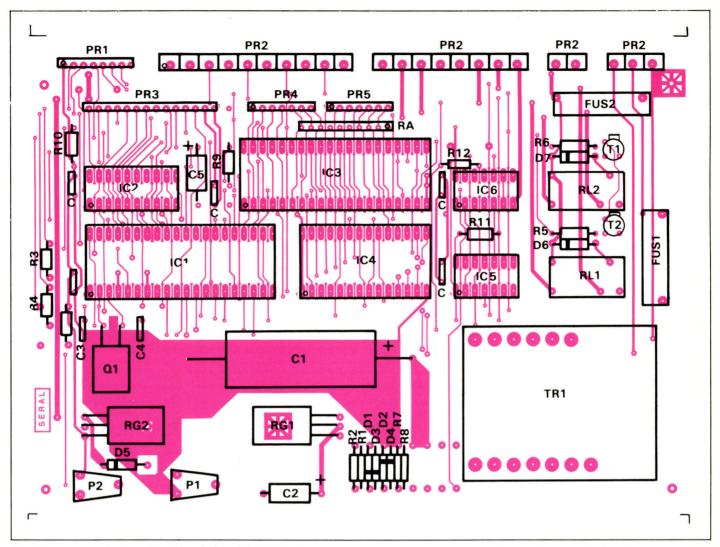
(ci-contre, en haut). — Circuit imprimé vu côté composants. Fig. 6b (ci-contre, en bas). — Circuit imprimé vu côté soudure.
